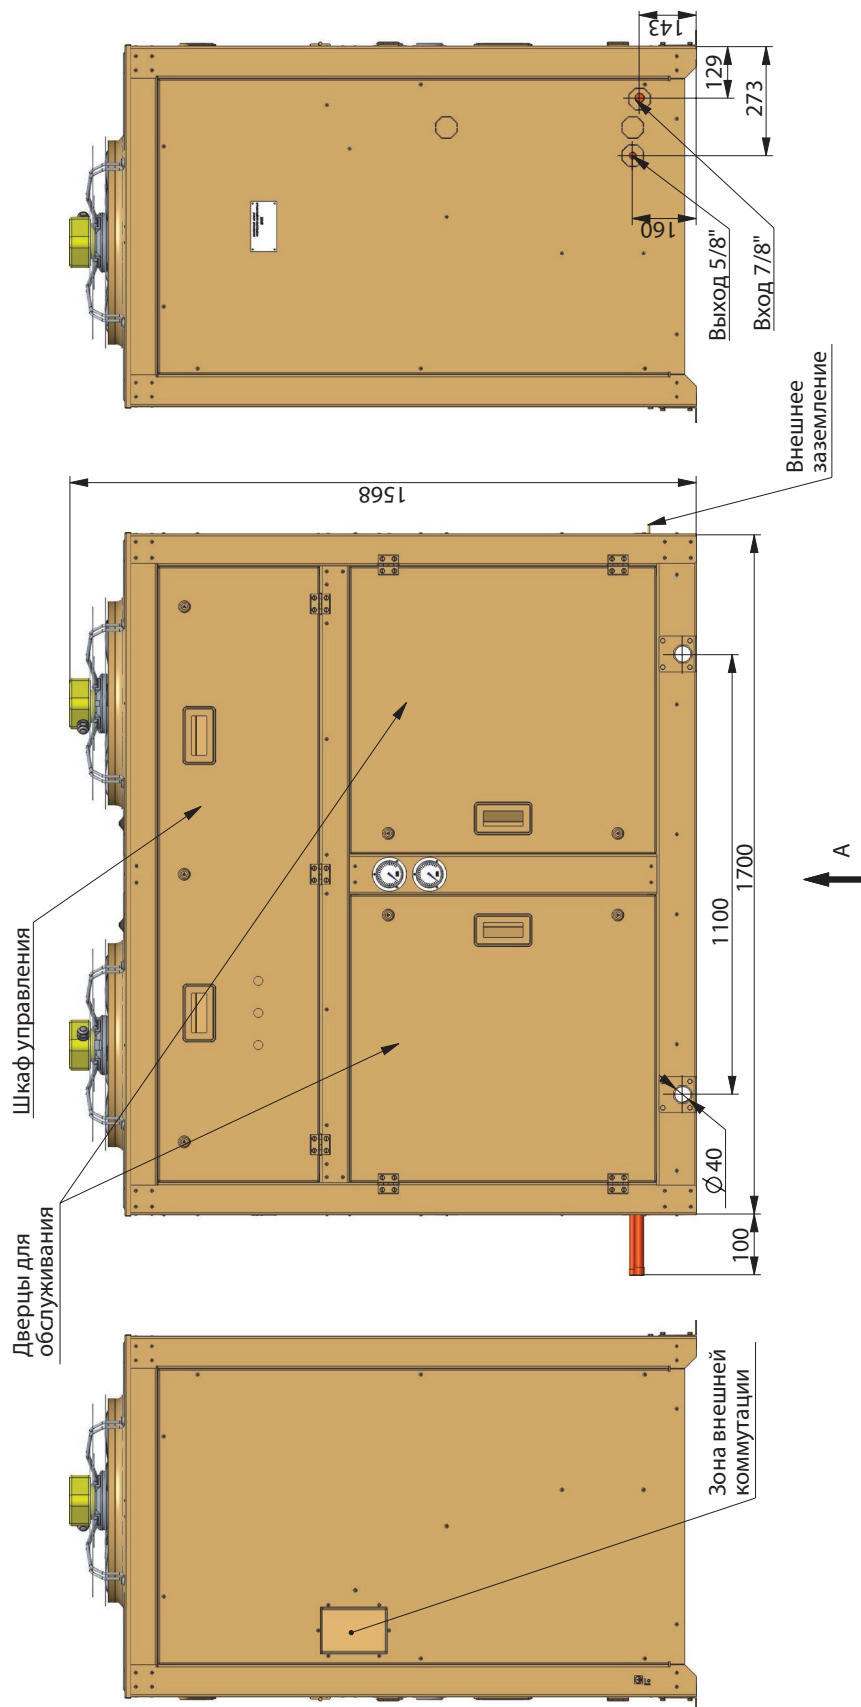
Агрегат компрессорный типа МАКК 320-301, -351
